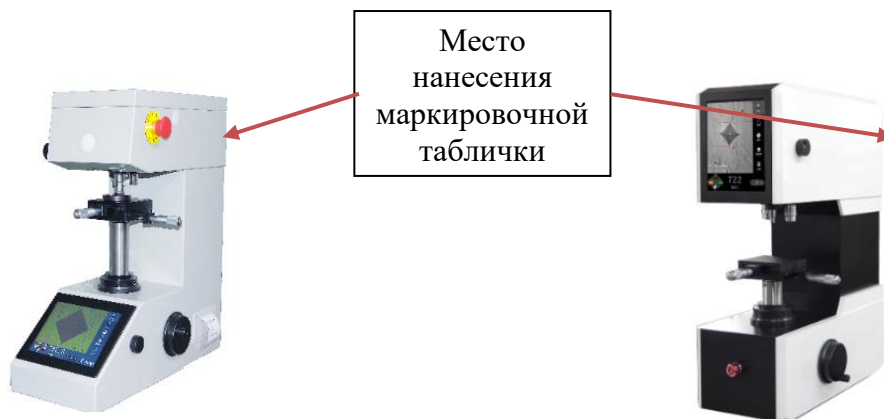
Общий вид твердомеров Виккерса MHVS-50V
